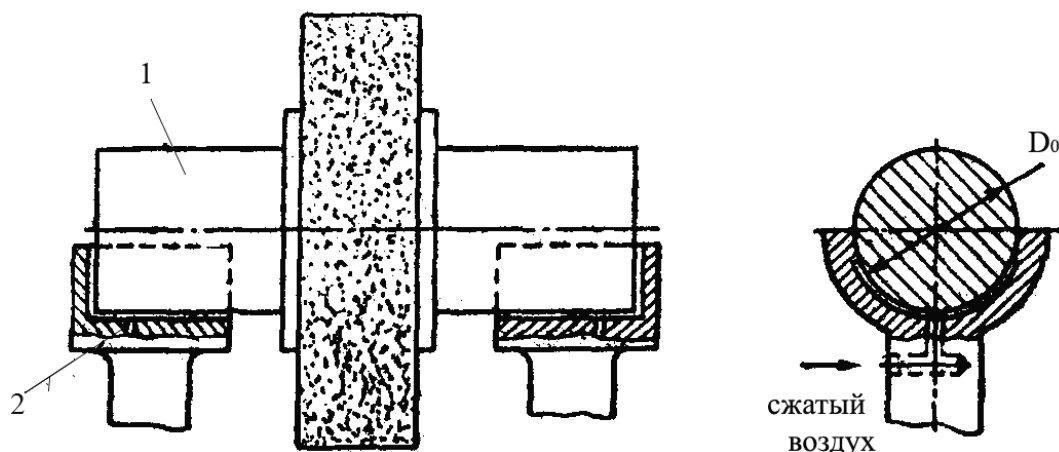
Схема балансировочного станка с аэростатическими опорами
